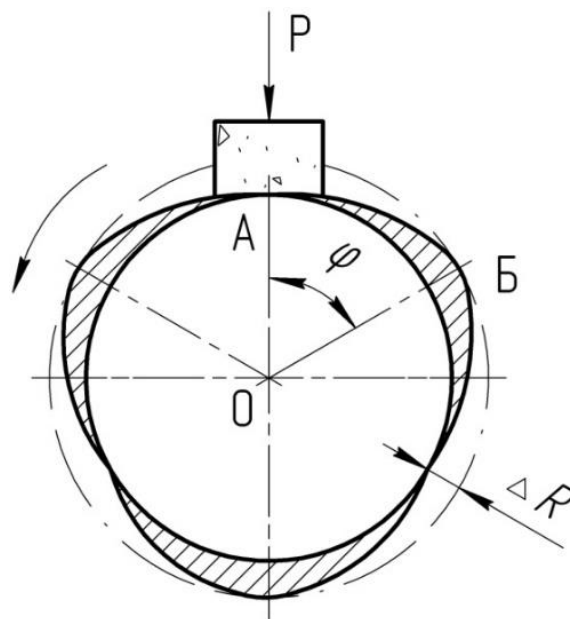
Схема обробки циліндричної поверхні абразивним бруском притисненим з однієї сторони
